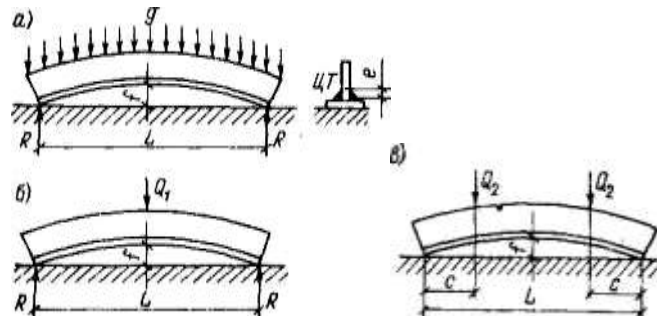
Продольная деформация сварной балки и схемы ее нагружения в сборочно-сварочном кондукторе
